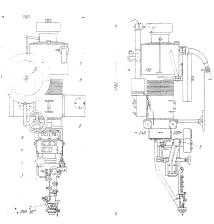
Чертеж общего вида сварочного автомата AБС с габаритными размерами и обозначениями основных узлов, расшифрованных в тексте
